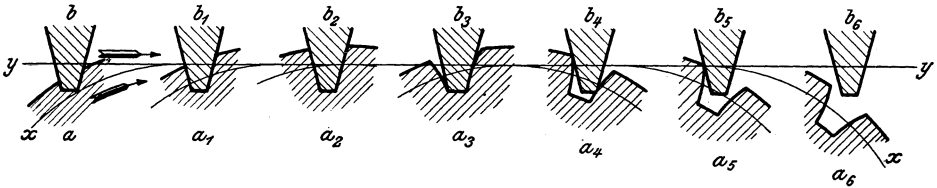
Mechanisches Entwickeln einer Zahnflanke.
